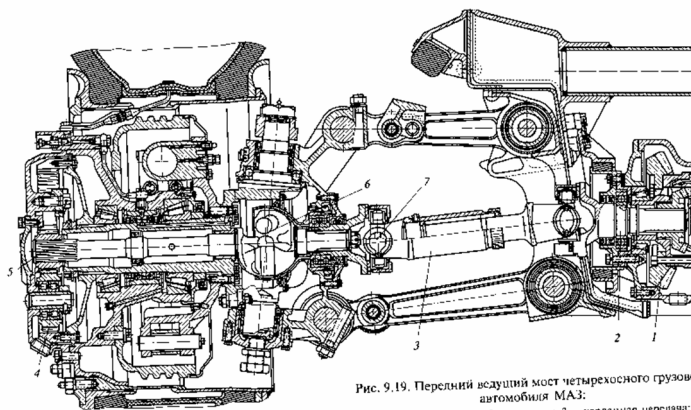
Передний ведущий мост четырехосного грузового автомобиля МАЗ: 1 — ведущий вал; 2 — карданный вал; 3 — промежуточный вал; 4 —
